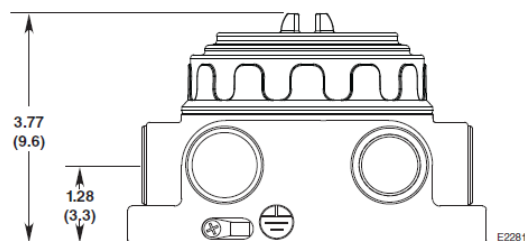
Размеры корпуса трансмиттера в дюмах (см).
